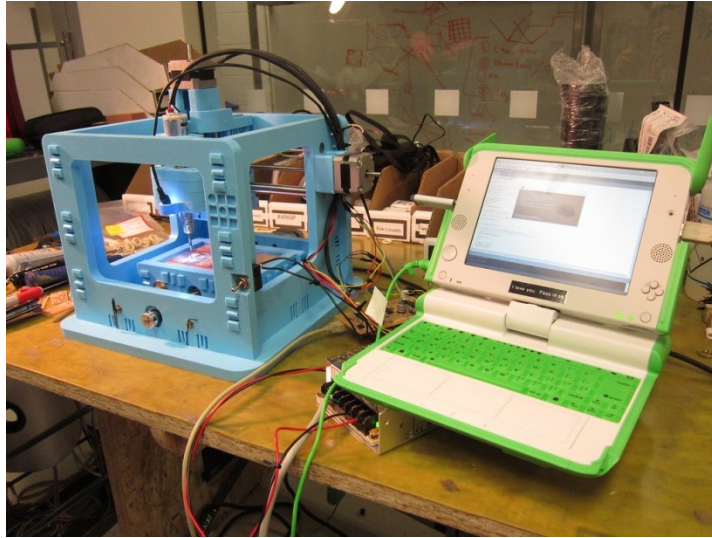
Фрезерний верстат з ЧПК MTM Snap
